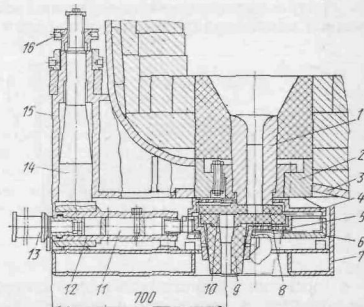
Шиберный затвор конструкции ВНИИметмаша
